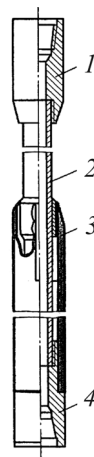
Шламометаллоуловитель типа ШМУ-О: 1 – трубный переводник; 2 – вал; 3 – кожух; 4 – переводник-база
